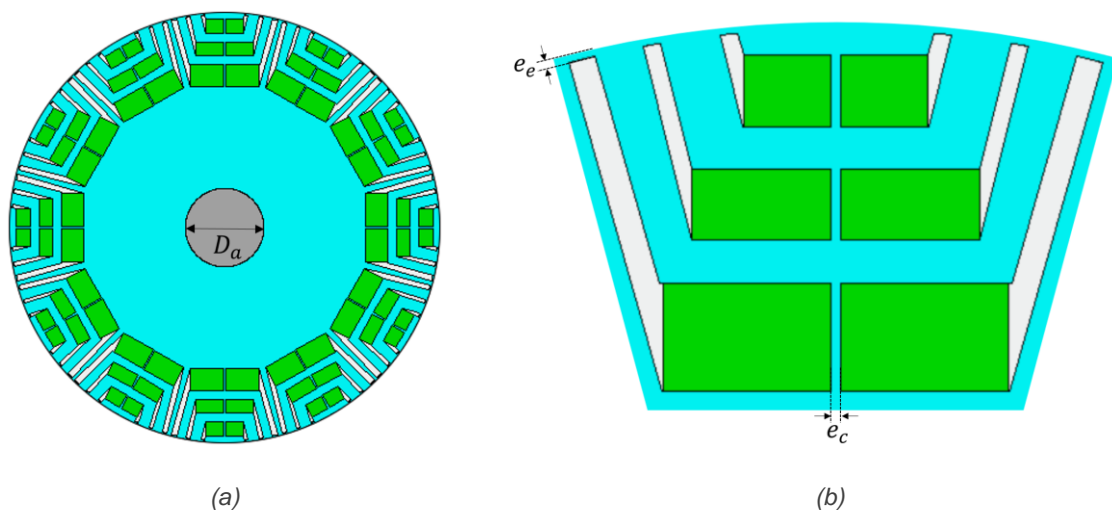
Rotor de la machine synchronreluctante assistée : (a) rotor complet et (b) un pôle du rotor
